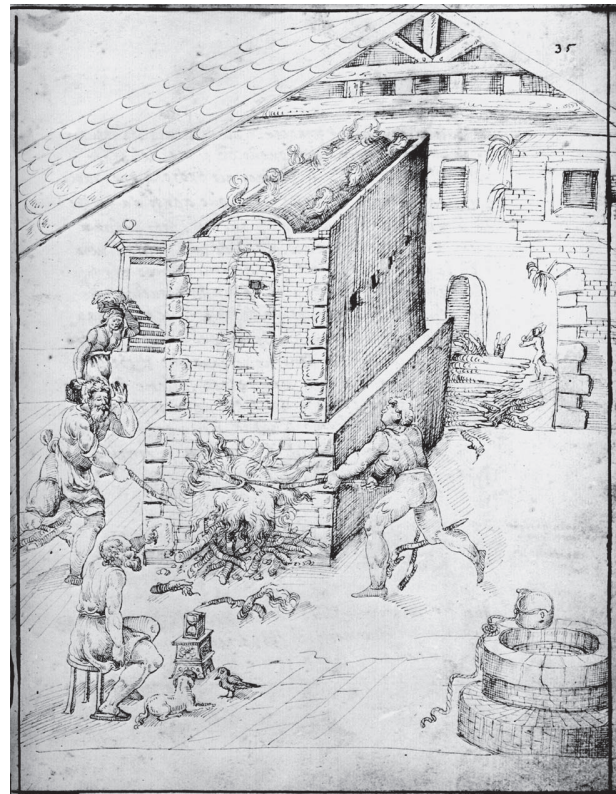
Stehender Ofen mit rechteckigem Grundriss zur Majolica-Produktion in Italien. Offensichtlich vollständig oberirdisch errichtet. Der Feuerungsraum befindet sich auf dem Niveau des Werkstattbodens. Cipriano Piccolpasso, I tre libri dell'arte del vasaio, 1558 (Piccolpasso Buch 1, fol. 35r aus: Lightbown/Caiger-Smith [Anm. 4]).
